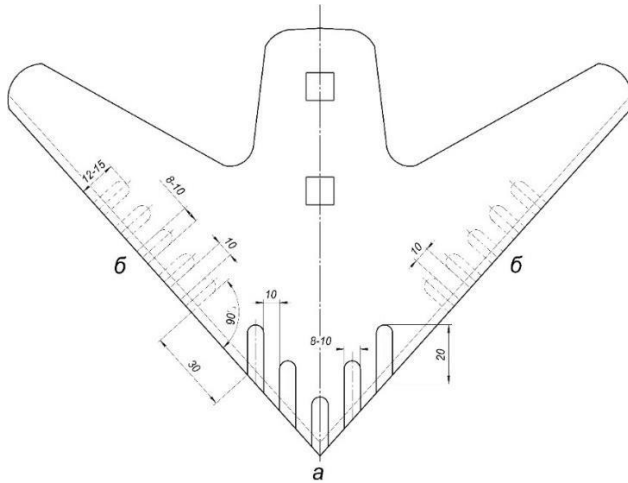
Схема наплавлення зміцнюючих смуг на поверхню стрілкової лапи культиватора: а – носок; б – крила [26]
